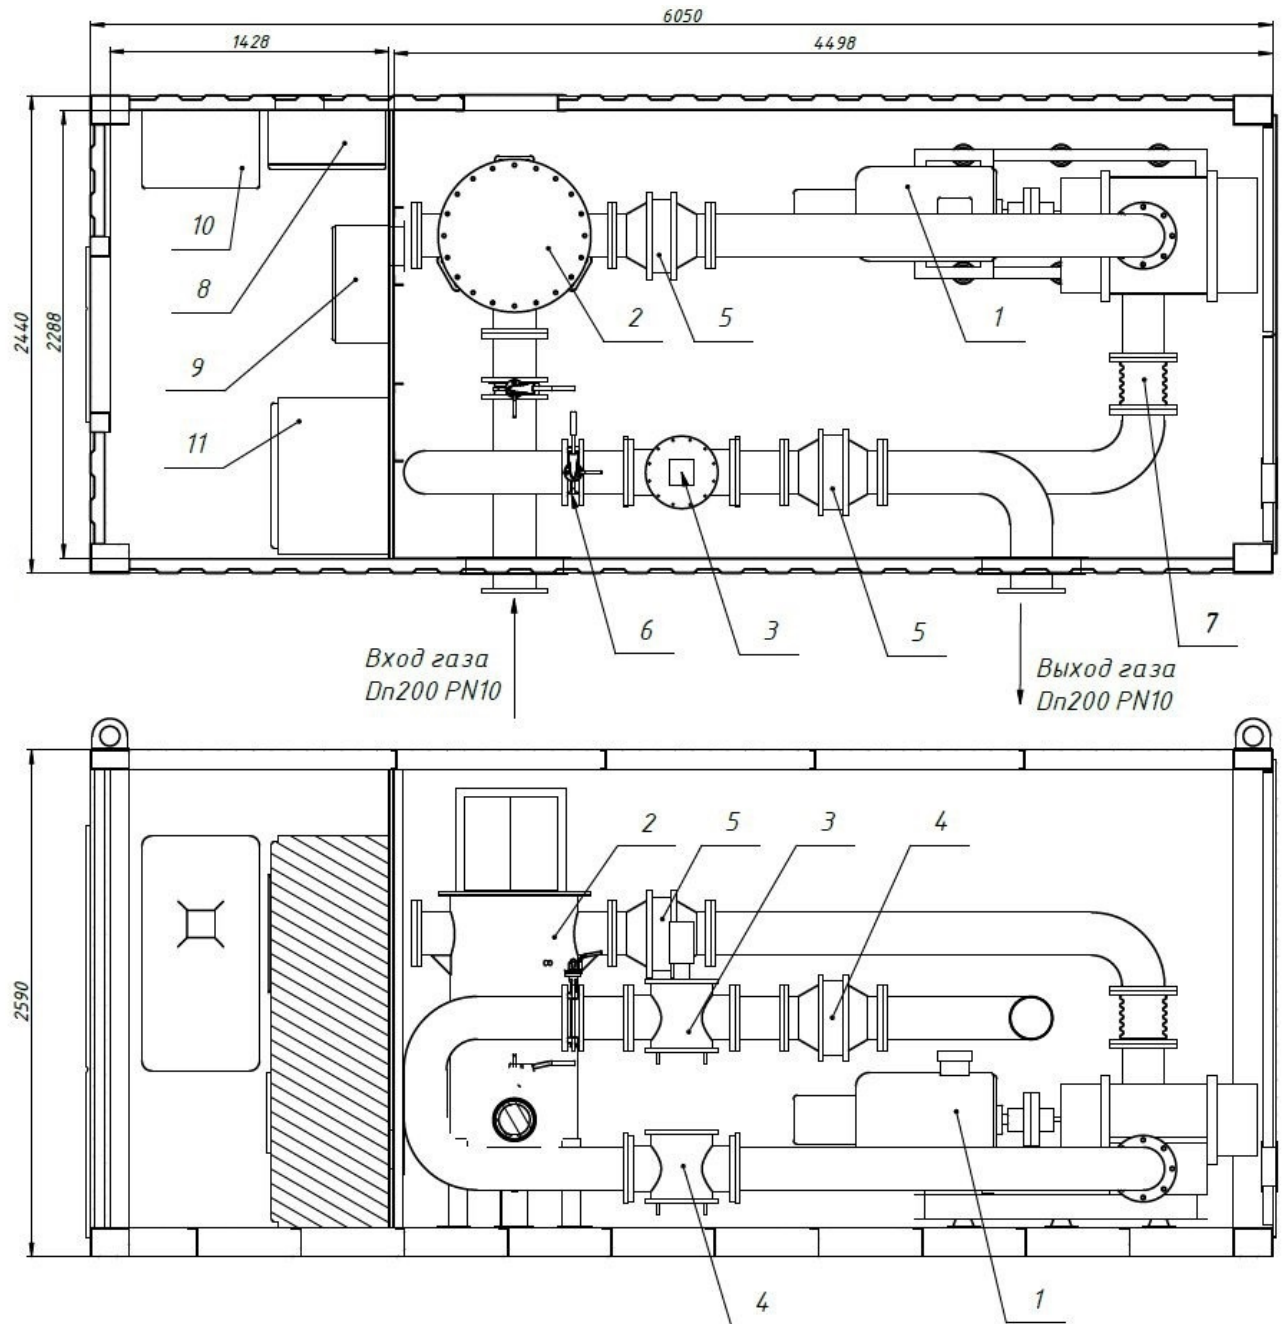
габаритные размеры и основные компоненты Газокомпрессорной станции ЧЕЛЯБГАЗМАШ – 1500С (1 - Компрессор-воздуходувка 2500 м<sup>3</sup>/мин, 45 кВт, 2 - Сепаратор, 3 - Запорный клапан, 4 - Расходомер, 5 - Огнепреградитель, 6 - Затвор поворотный дисковый DN200, 7 - Антивибрационное соединение, 8 - Шкаф распределения питания, 9 - Шкаф управления, 10 – Преобразователь частоты, 11- Шкаф газоанализатора.)
